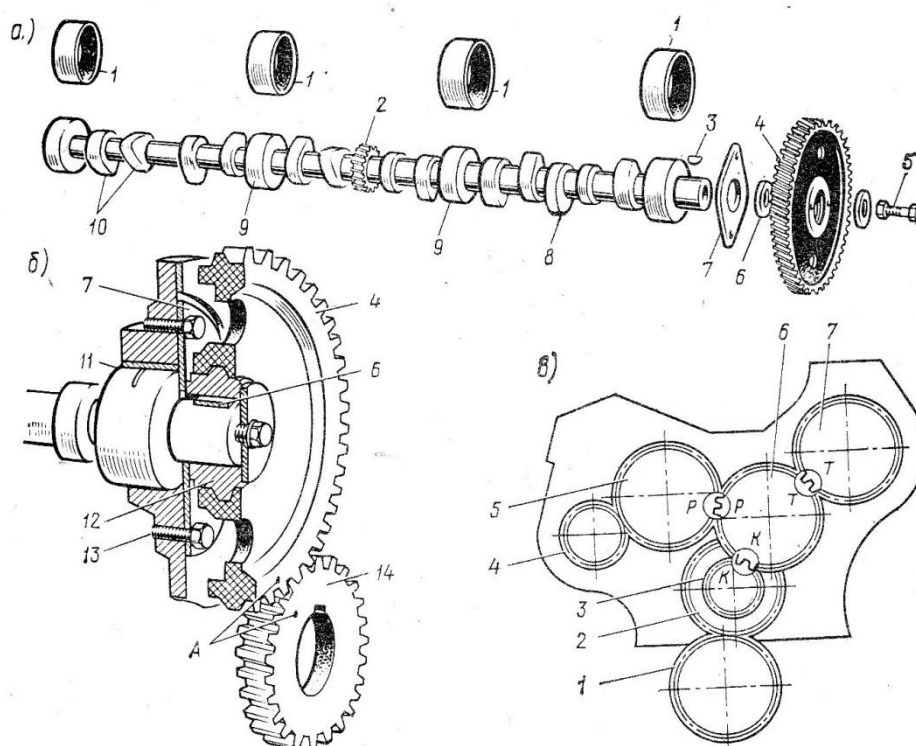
Распределительный вал (а) и его привод (б): 1 – подшипник; 2 – шестерня; 3 – шпонка; 4 – приводная шестерня; 5 – болт; 6 – распорное кольцо; 7 – упорный фланец; 8 – эксцентрик; 9 – опорная шейка; 10 – кулачки; 11 – передний подшипник; 12 – ступица приводной шестерни; 13 – болт; 14 – ведущая шестерня;
